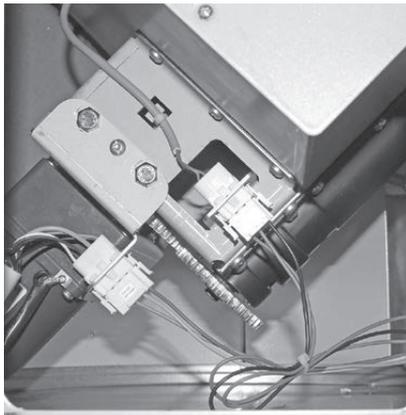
Inserire i connettori del motore della coclea e dell'interruttore di prossimità
